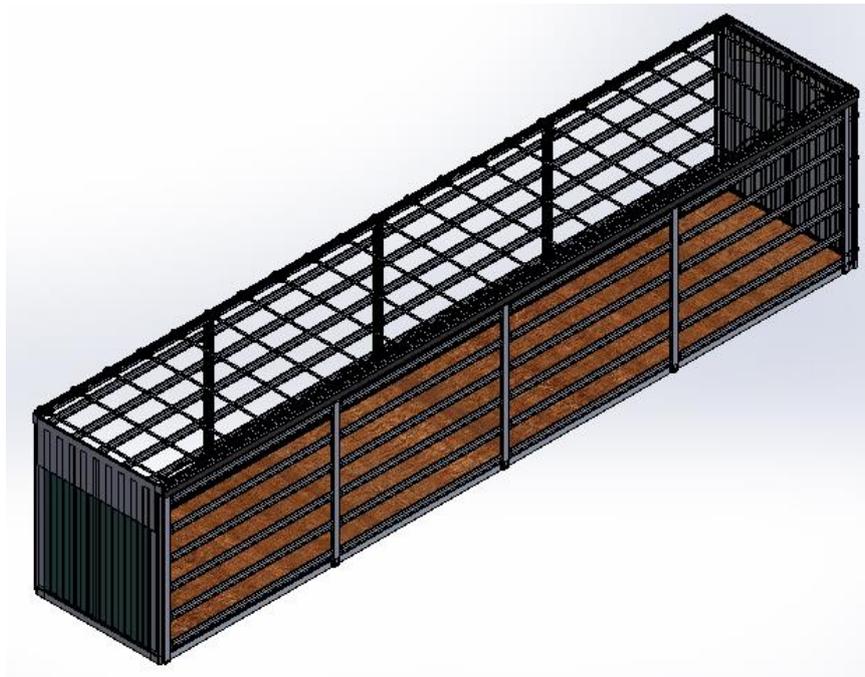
Colocación de los perfiles para sobrecartola apilables
